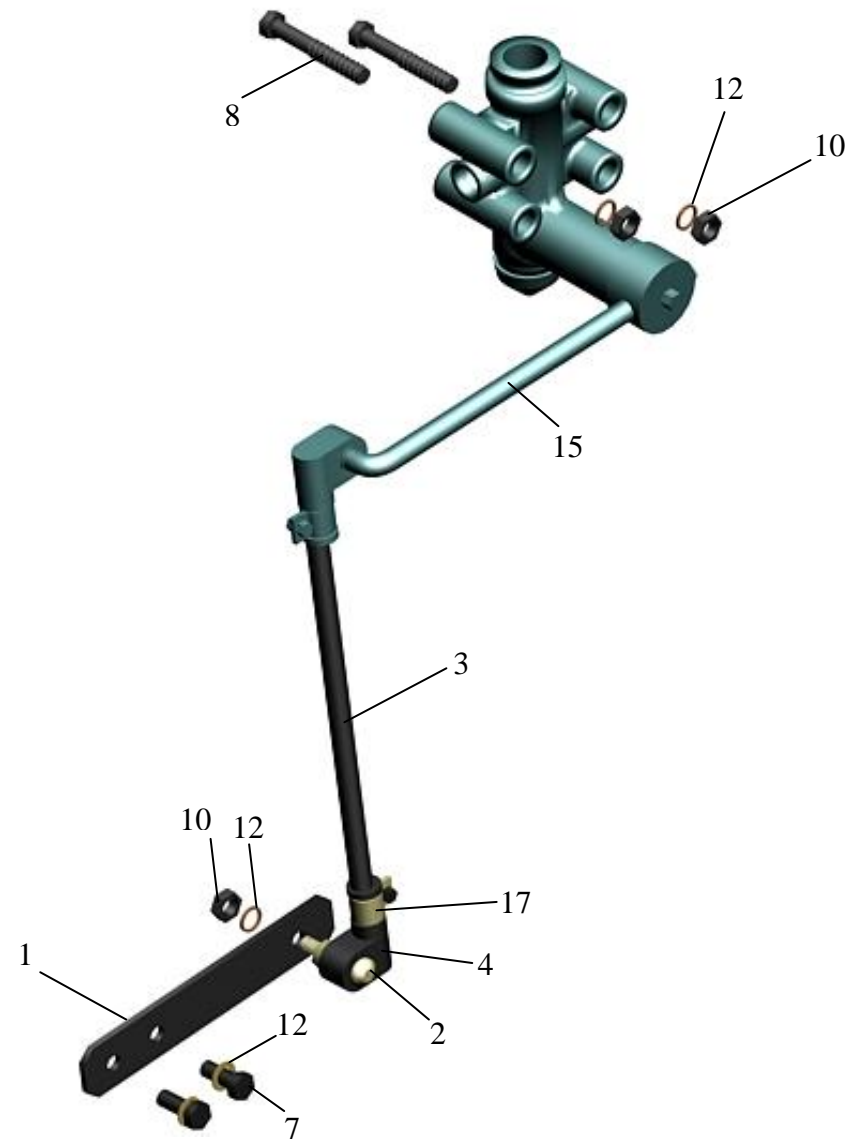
Установка регулятора положения кузова АКСМ 333-210300.000
